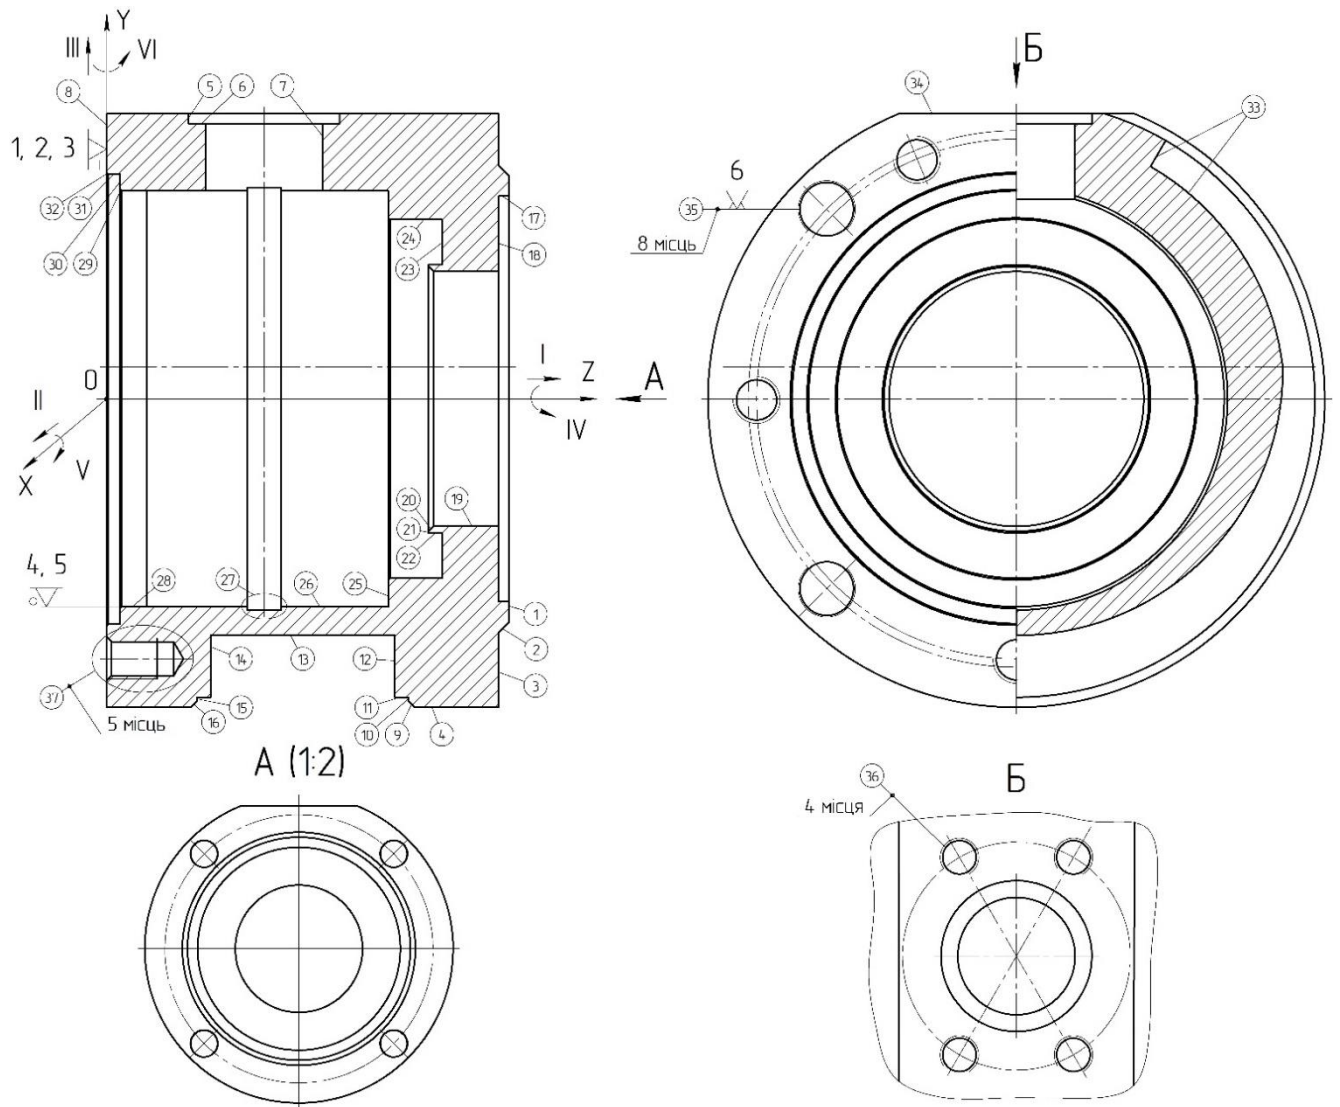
Ескіз деталі «Корпус» із нумерованими поверхнями
